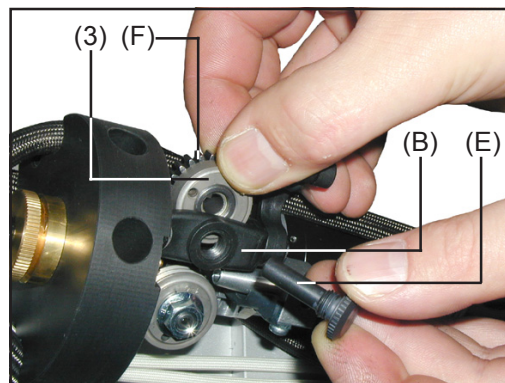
Druckrolle mit „Triebzahnrad Schwenkhebel“ aus- und einbauen
